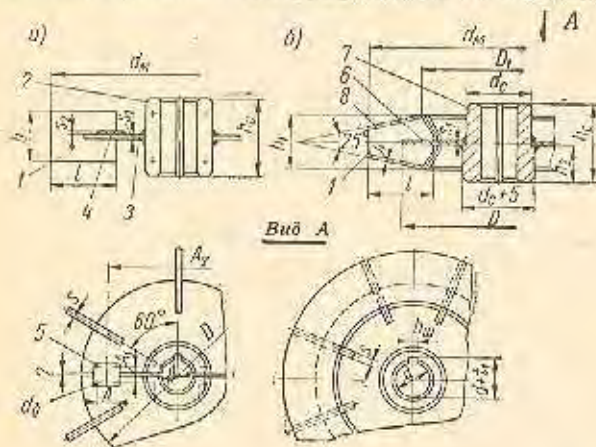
Конструкция стальных сварных турбинных перемешивающих устройств (типы а и б) по МН 5874—66: а — тип 5 (шифр 50), открытые; б — тип 6 (шифр 60), закрытые: 1 — лопасть; 2 — ступица из двух половин; 3 — диск из двух половин; 4 — плавник; 5 — болты с гайками и шайбами; 6 — диск; 7 — ступица; 8 — конус
